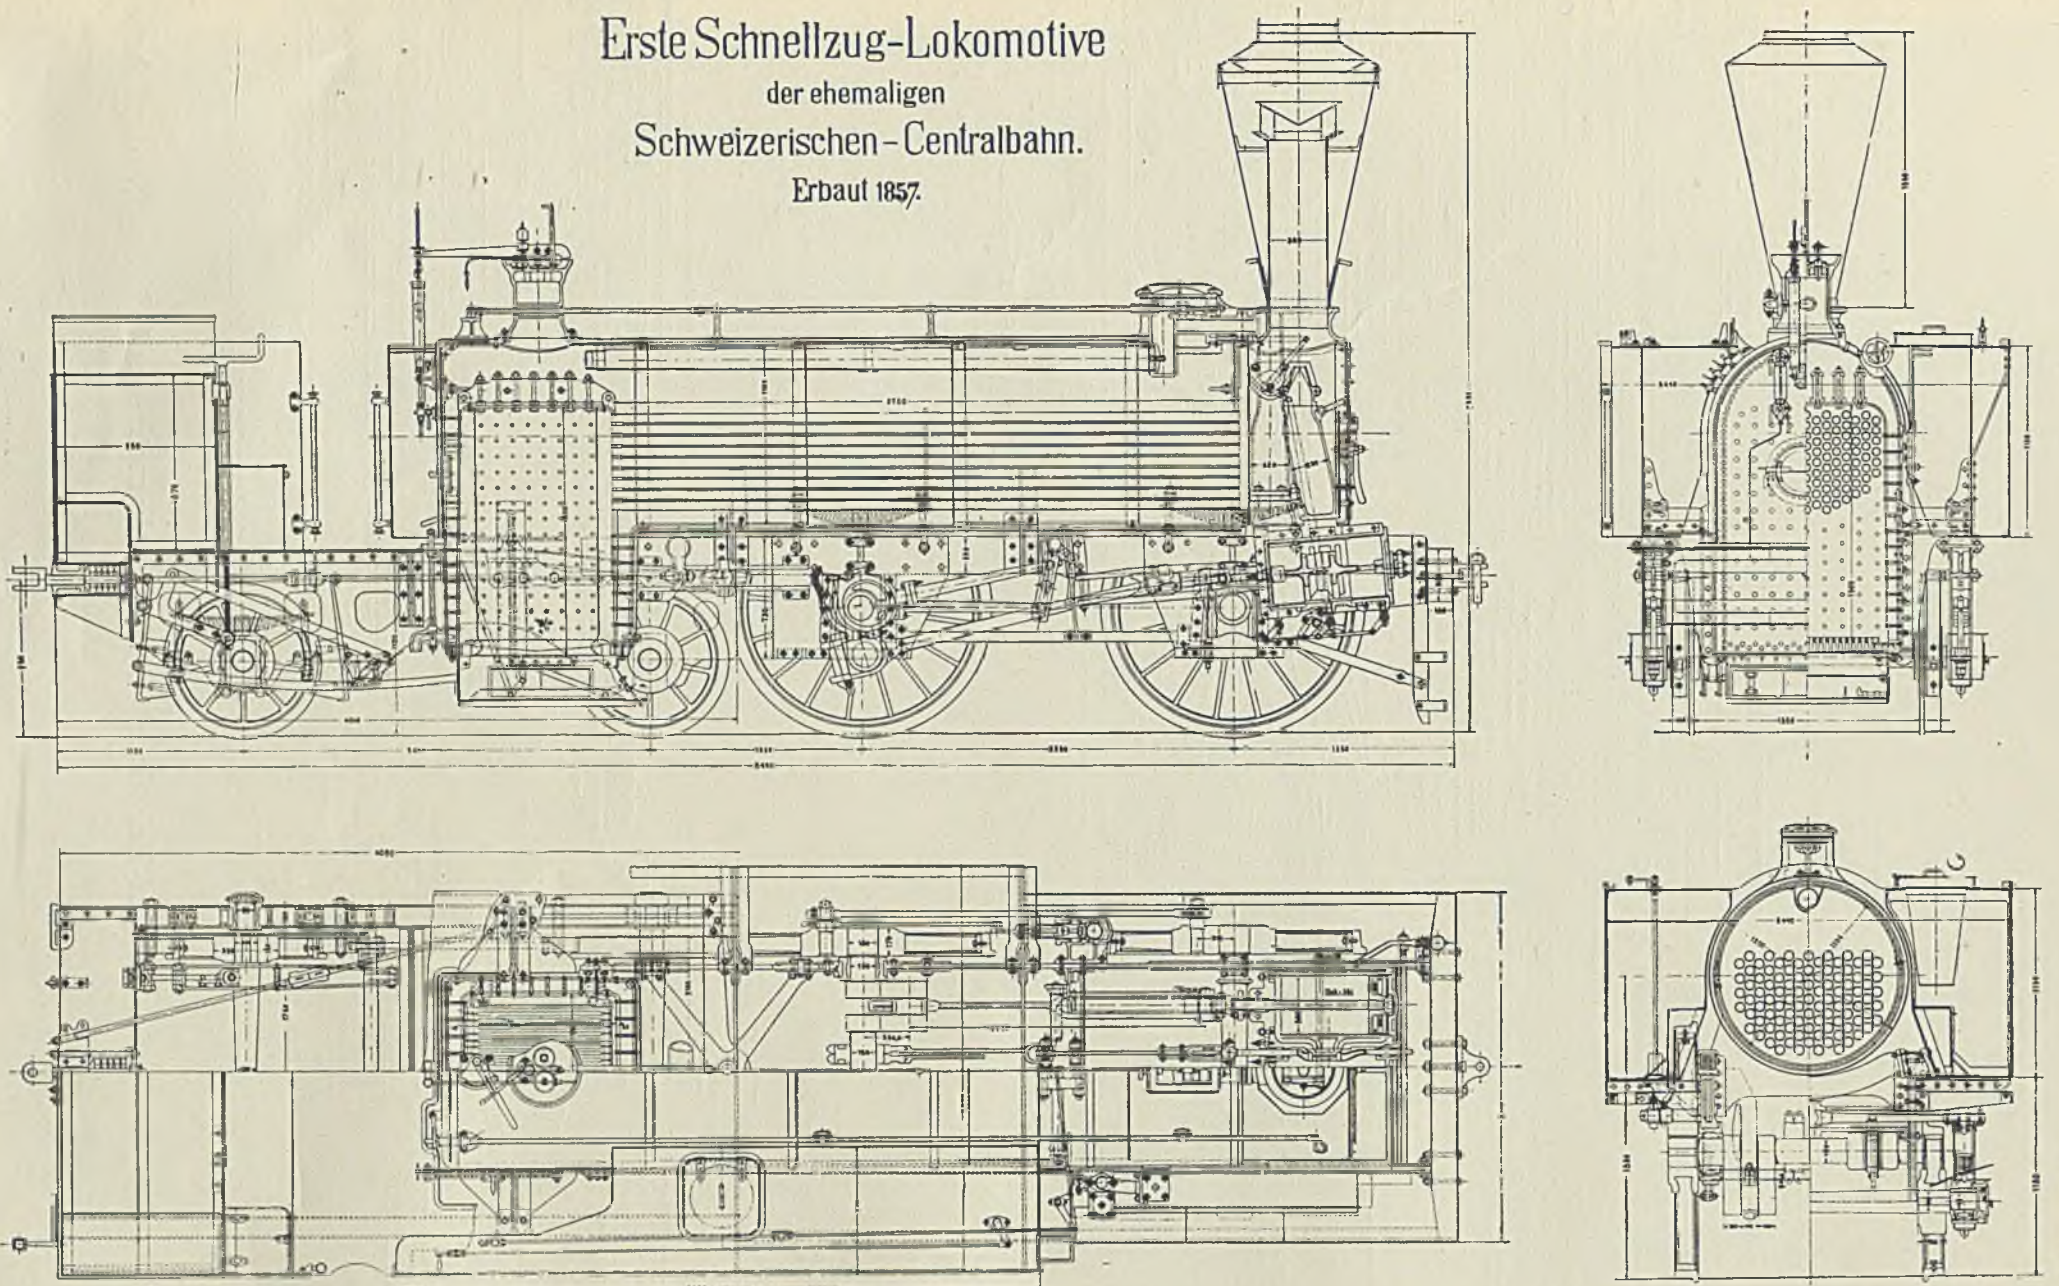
Längsschnitt, 1/2-Wagrechtsschnitt, 1/2-Grundriss, Querschnitte. Masstab ca. 1:50.
